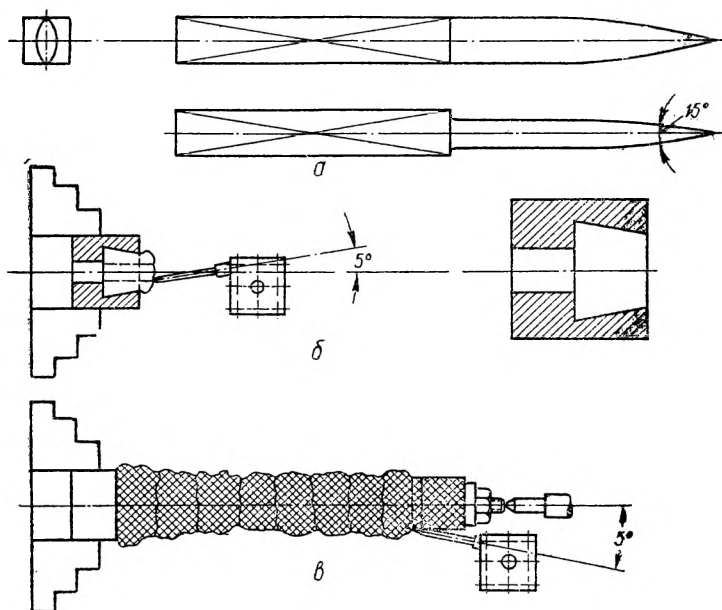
Шарошка для обработки абразивных шлифовальных кругов.
